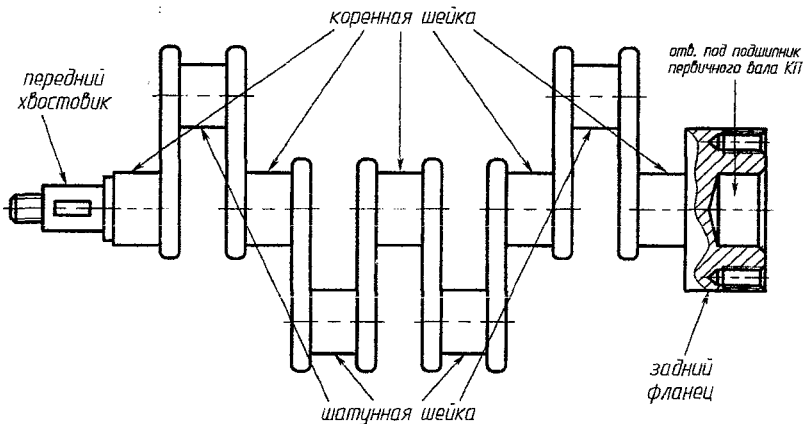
Основные конструктивные элементы коленчатого вала двигателя автомобиля ВАЗ
